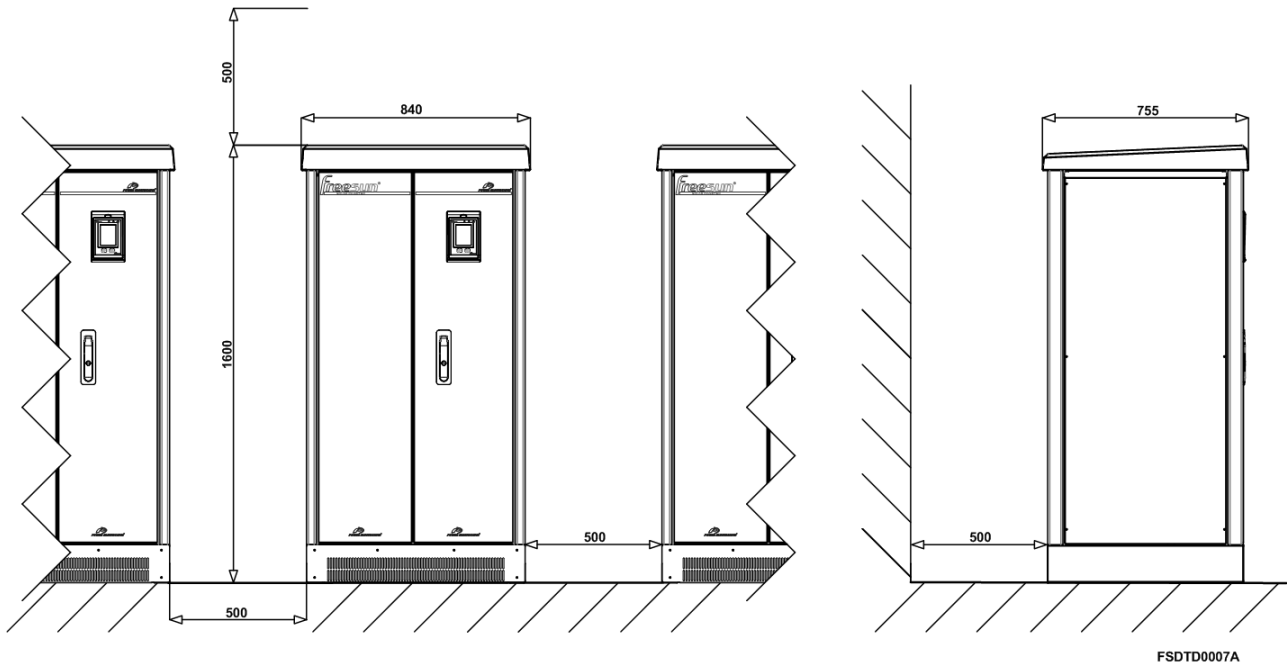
Instalación del Talla 3 Outdoor con bloque de hormigón de cimentación.
